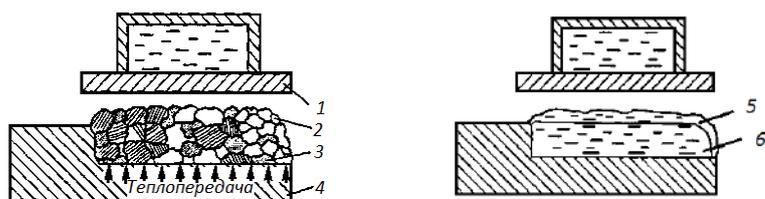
Схема способа индукционной наплавки порошкообразной шихтой:
